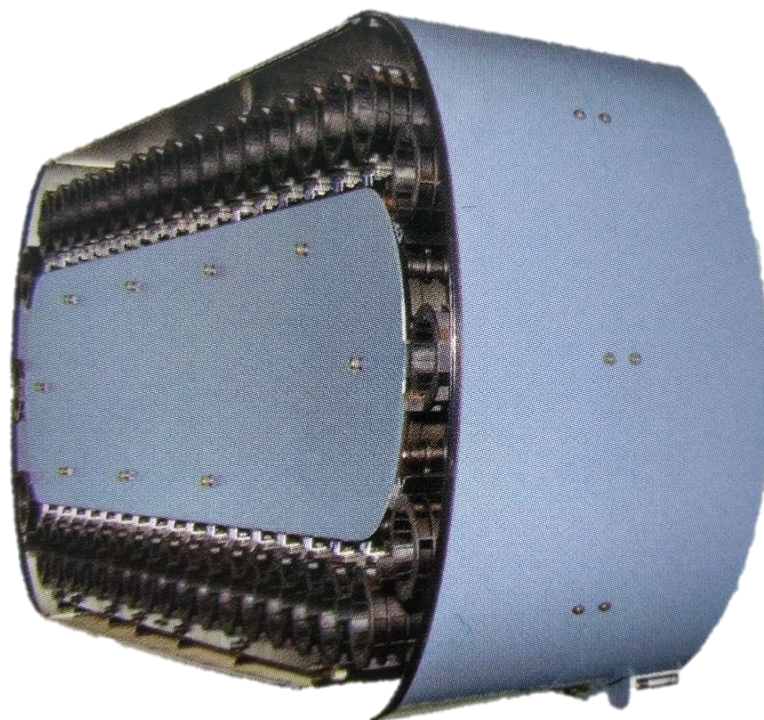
Інструментальний магазин типу ланцюгового конвеєра верстатів Fulland, серія DMC [5]
